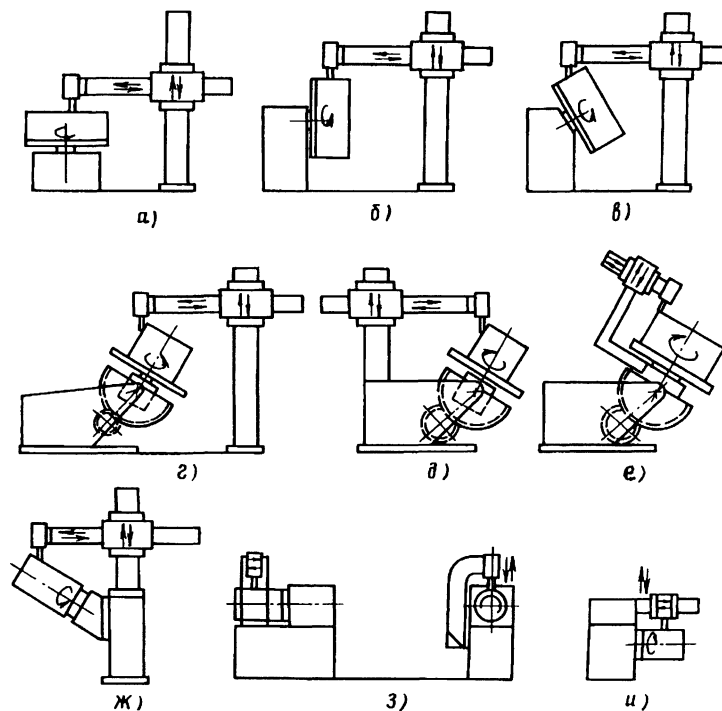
Типовые схемы компоновки установок и станков для дуговой сварки круговых швов и наплавки поверхностей тел вращения изделий, закрепляемых консольно
